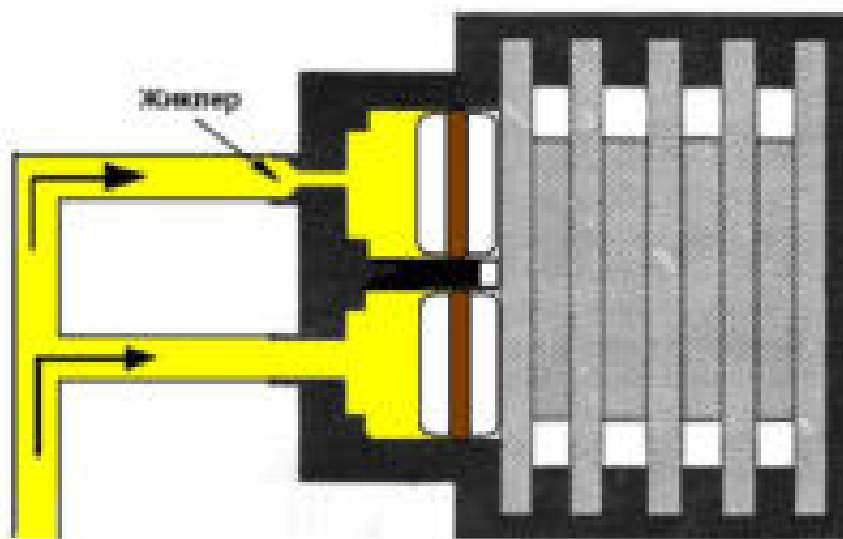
Установка жиклера на входе в исполнительный цилиндр для обеспечения плавного нарастания давления.
